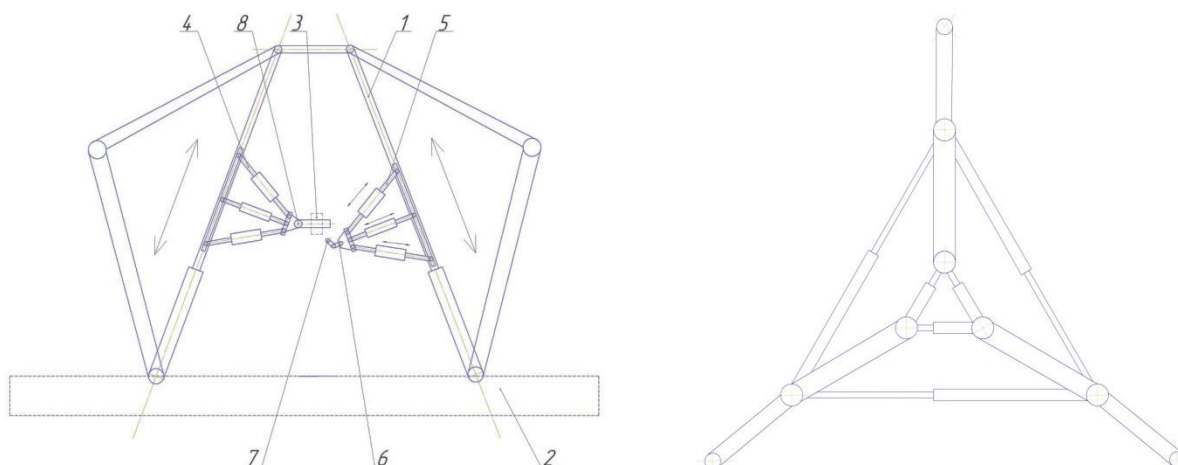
Схема обработки зубчатого колеса на станке-роботе
